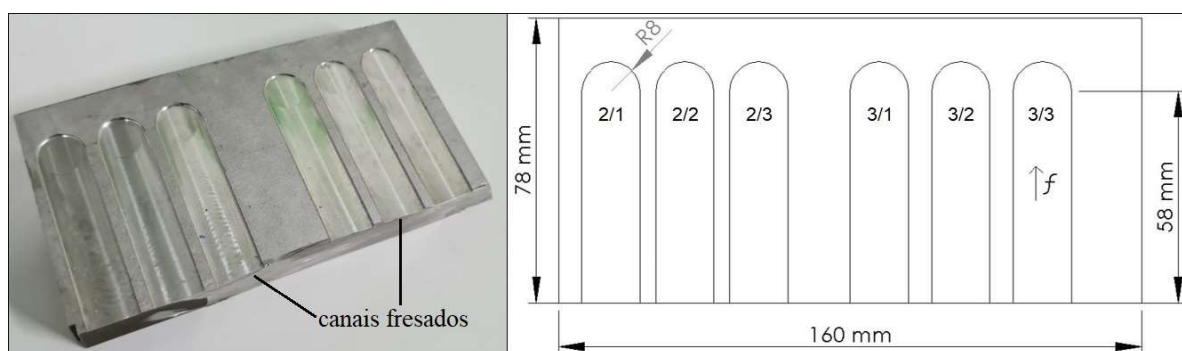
Amostra fresada nas condições 2 e 3 com dimensões e sentido de avanço da usinagem.
